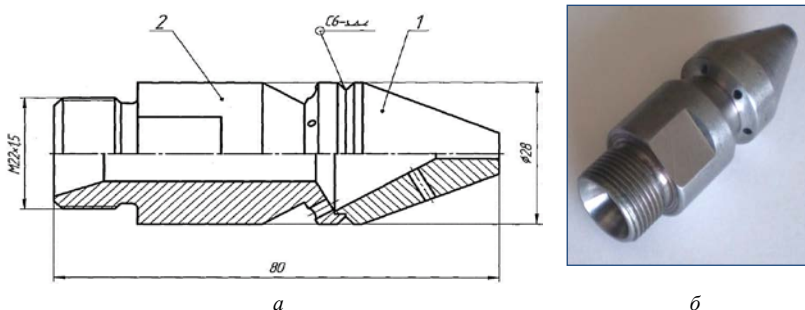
Конструкция реактивной головки машины УПД-120: а – головка в сборе; б – общий вид головки; 1 – корпус; 2 – передняя часть
